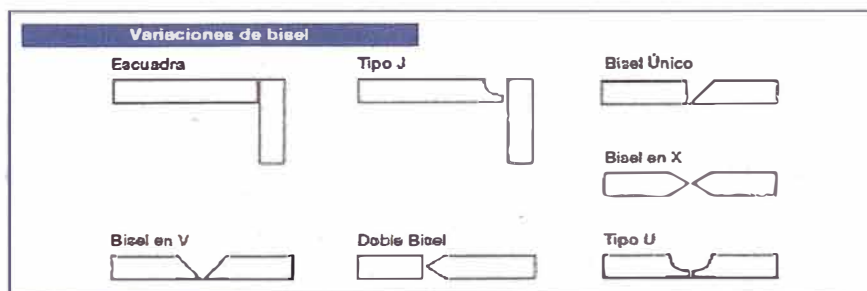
Tipos de biseles (Fuente: Manual de Soldadura Indura)
